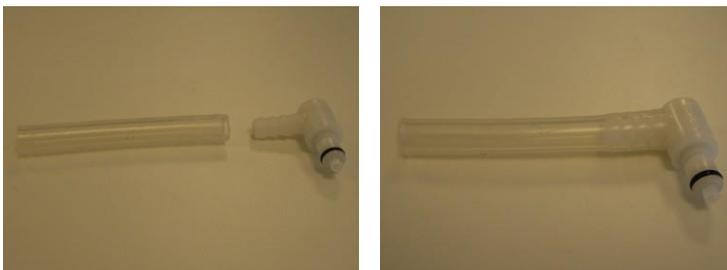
Collegamento della porzione più lunga del tubo a vuoto al raccordo del connettore rapido
